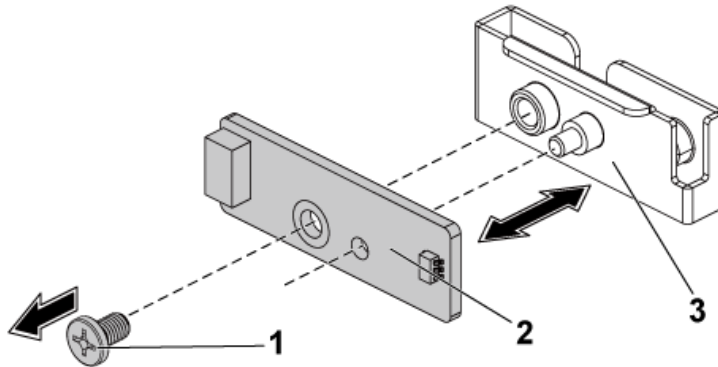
Entfernen und Einsetzen der Sensorplatte
